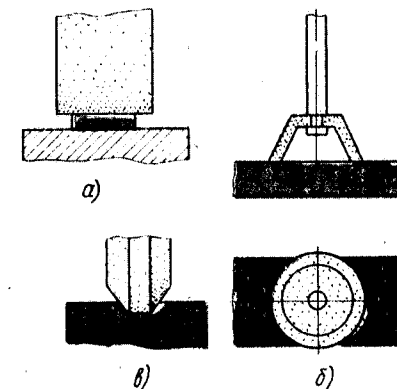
Шлифование заготовок на плоскошлифовальных станках
